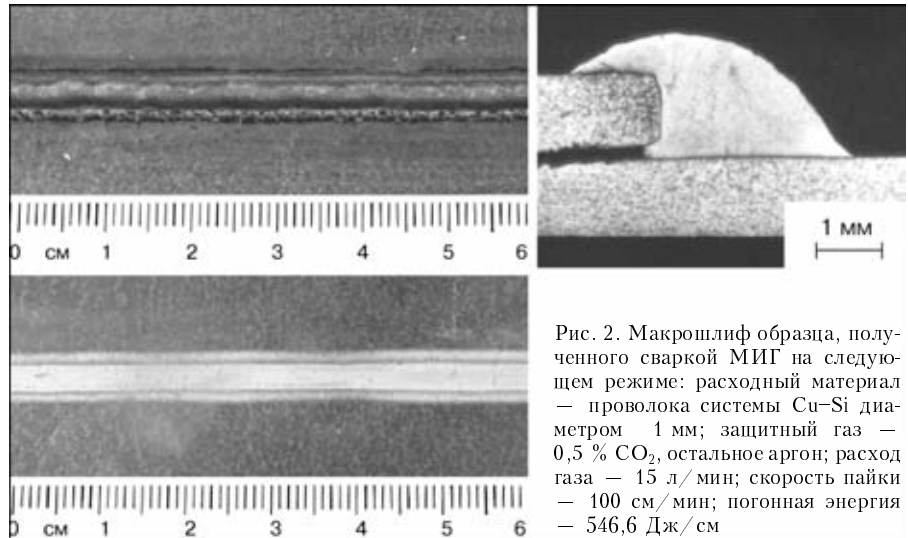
Макрошлиф образца, полученного сваркой МИГ на следующем режиме: расходный материал — проволока системы Cu-Si диаметром 1 мм; защитный газ — 0,5 % CO₂, остальное аргон; расход газа — 15 л/мин; скорость пайки — 100 см/мин; погонная энергия — 546,6 Дж/см
